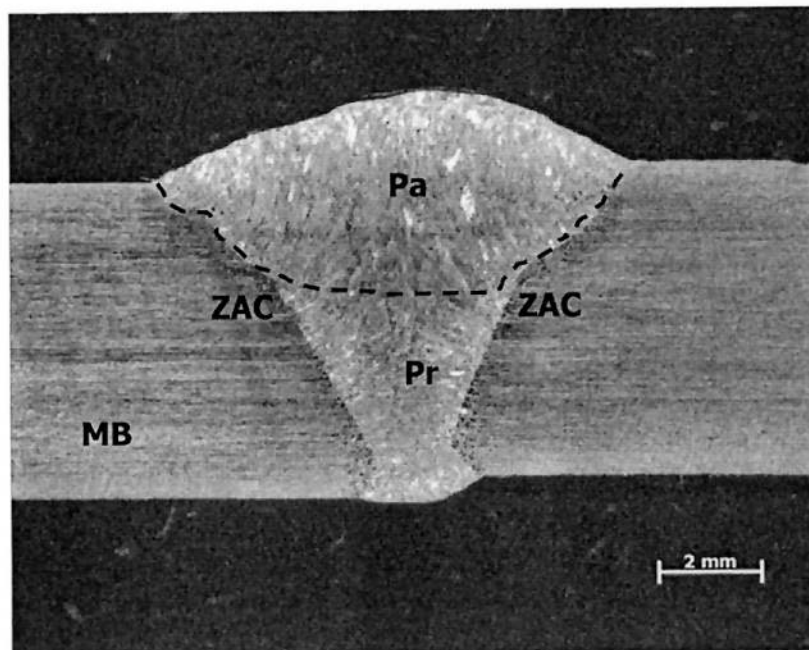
Macrografia da junta soldada do CP1.
